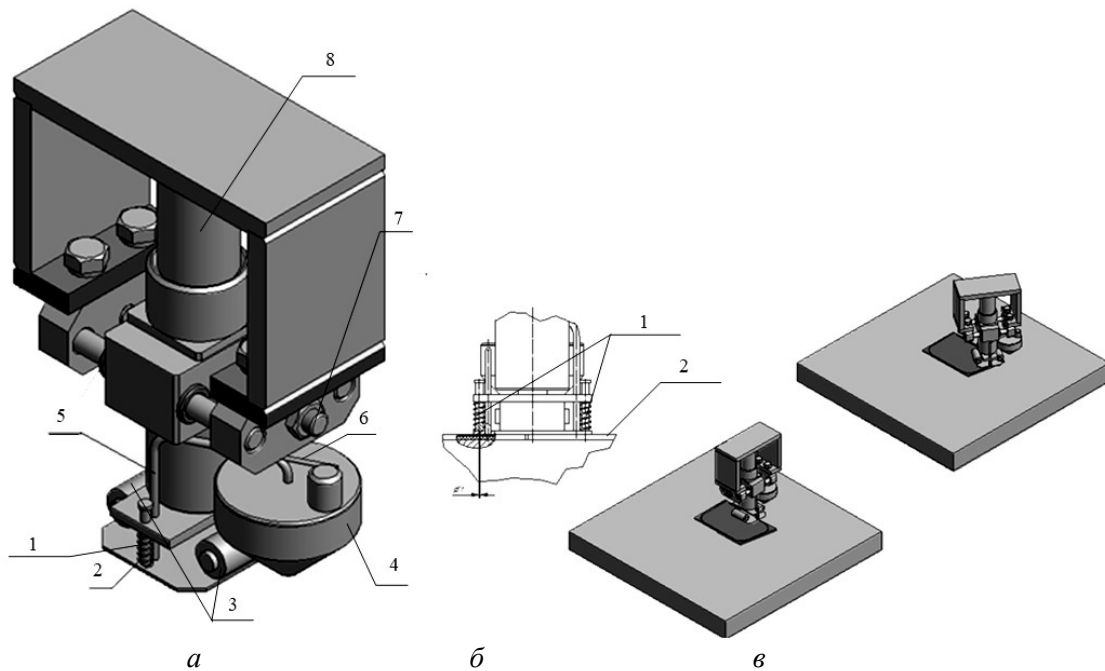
Головка для магнітно-абразивного полірування: а, б – конструкція; в – положення головки у процесі обробки
